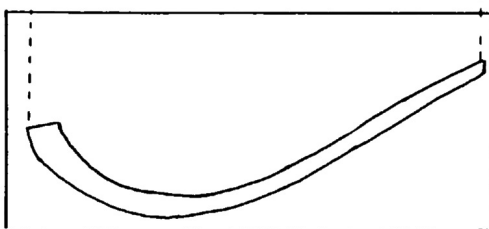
Чертеж заготовки для изготовления регелей гальюна. Этот брусок вырезается сначала по виду сверху, а затем на нем рисуется вид сбоку и вырезается. Вам потребуются небольшие навыки резьбы.
